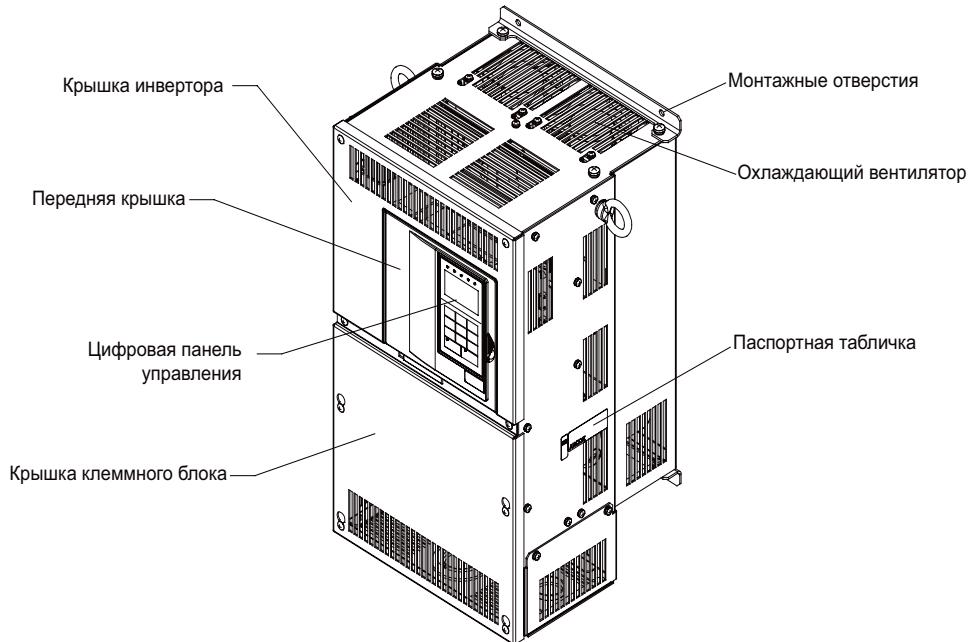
Внешний вид инвертора (22 кВт и больше)
